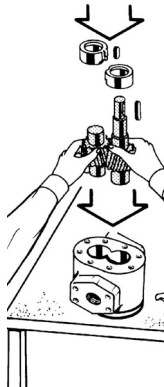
Сдвигание валов и подшипников скольжения с клиновой шпонкой в корпус по вертикали
